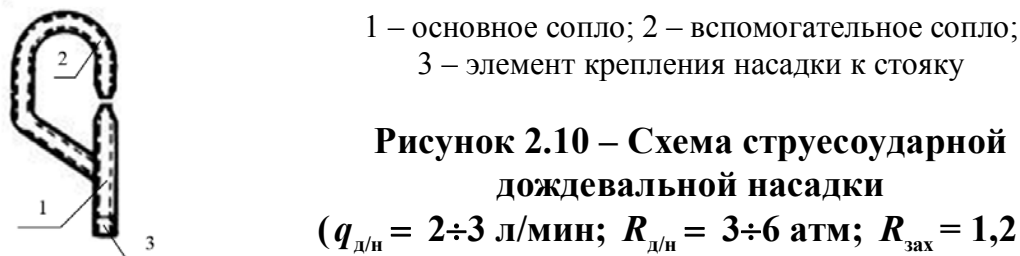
Схема струесоударной дождевальной насадки
